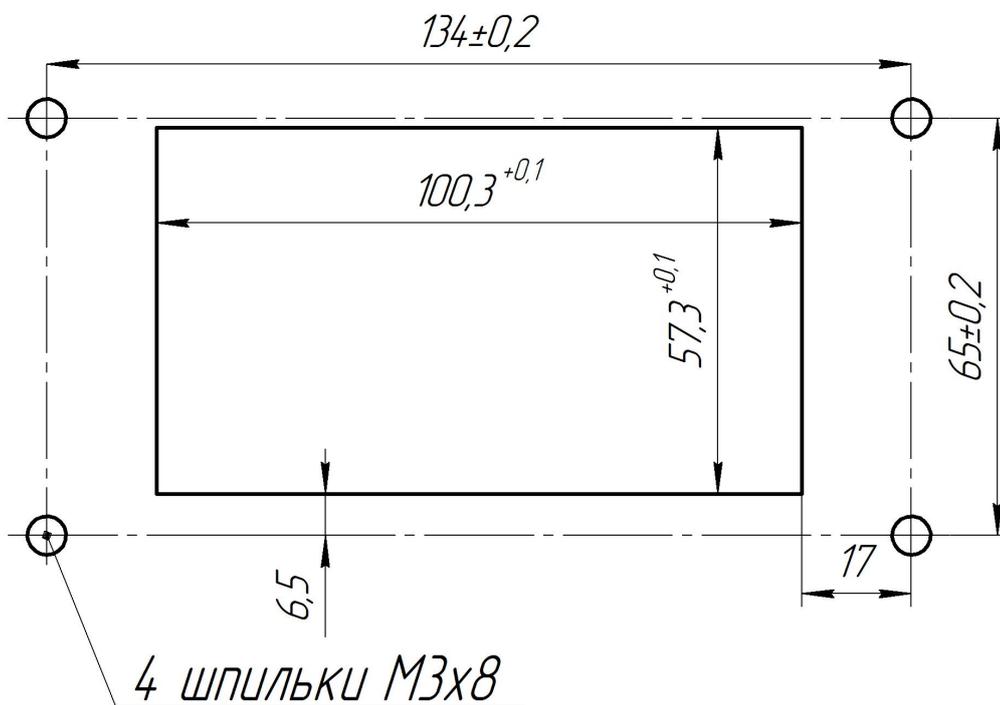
Разметка для крепления устройства (вид со стороны установки ЖКИ)
